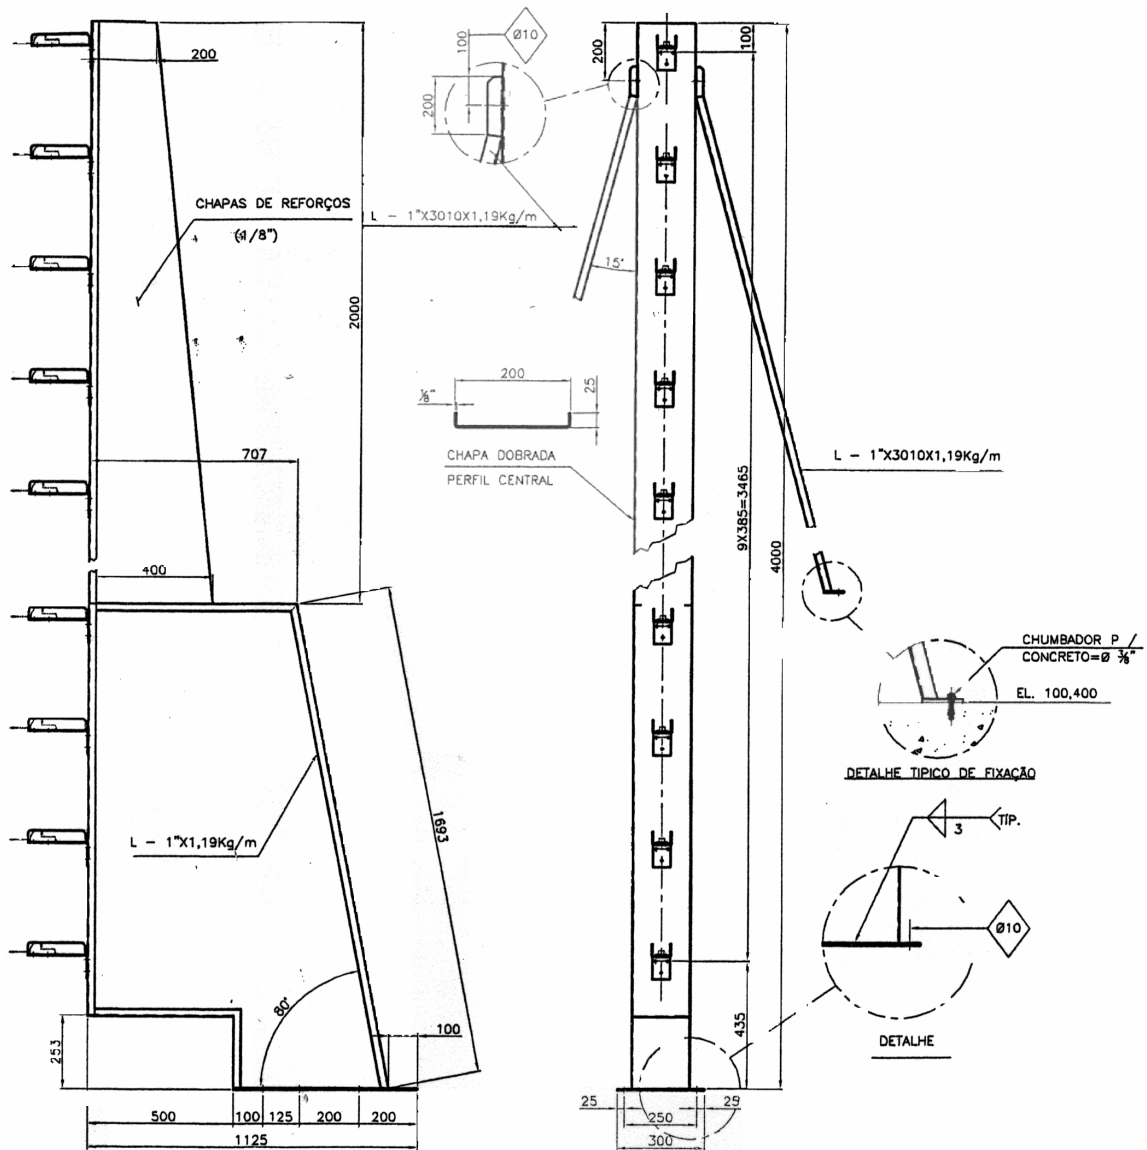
Projeto do suporte metálico dos sensores
